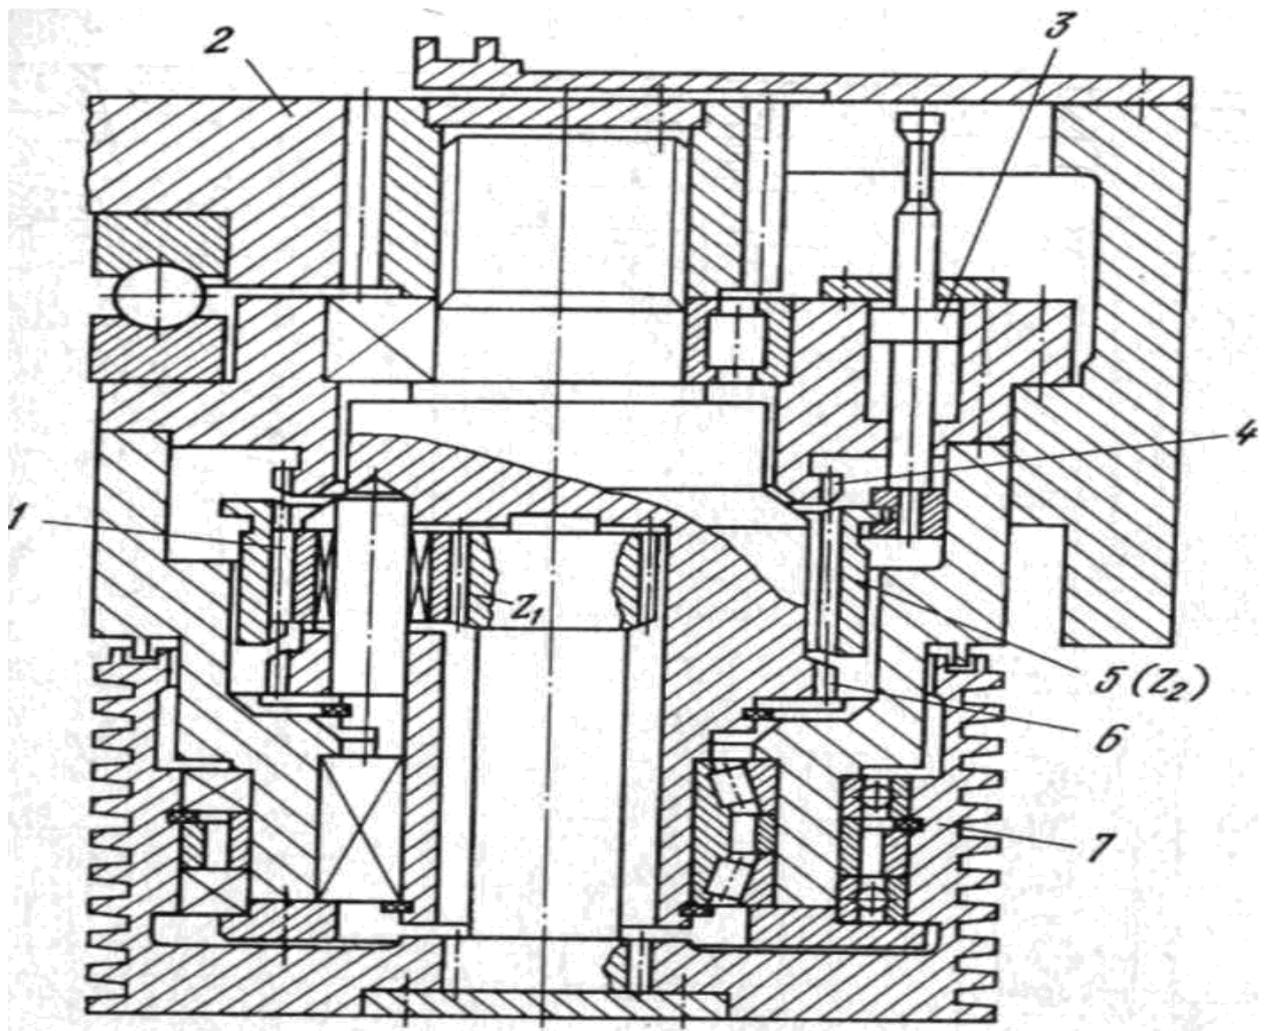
Схема планетарной двухскоростной коробки скоростей.
